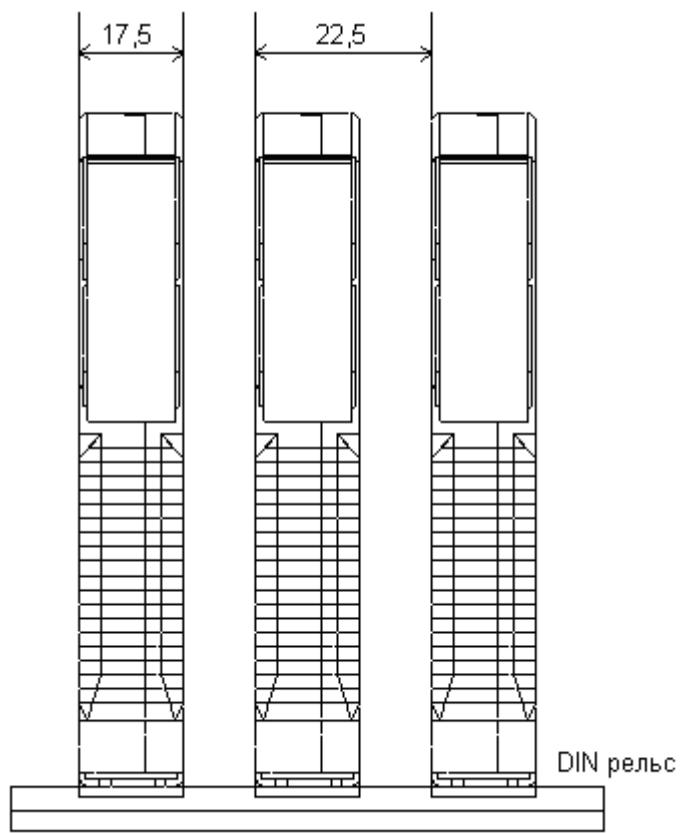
Установочные габаритные размеры преобразователя ET 383
